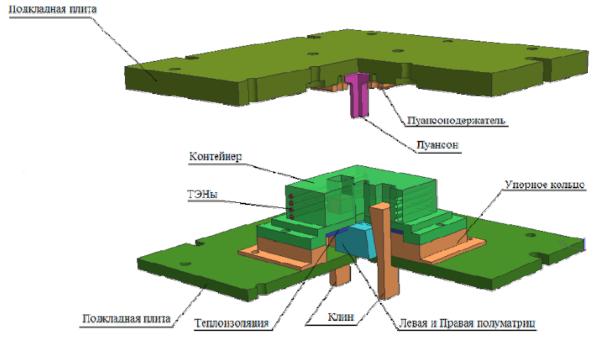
Предлагаемая конструкция установки для выдавливания переменного сечения заготовок лопаток
